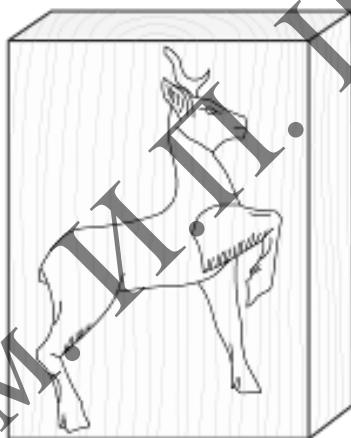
Пример расположения эскиза изделия на заготовке
